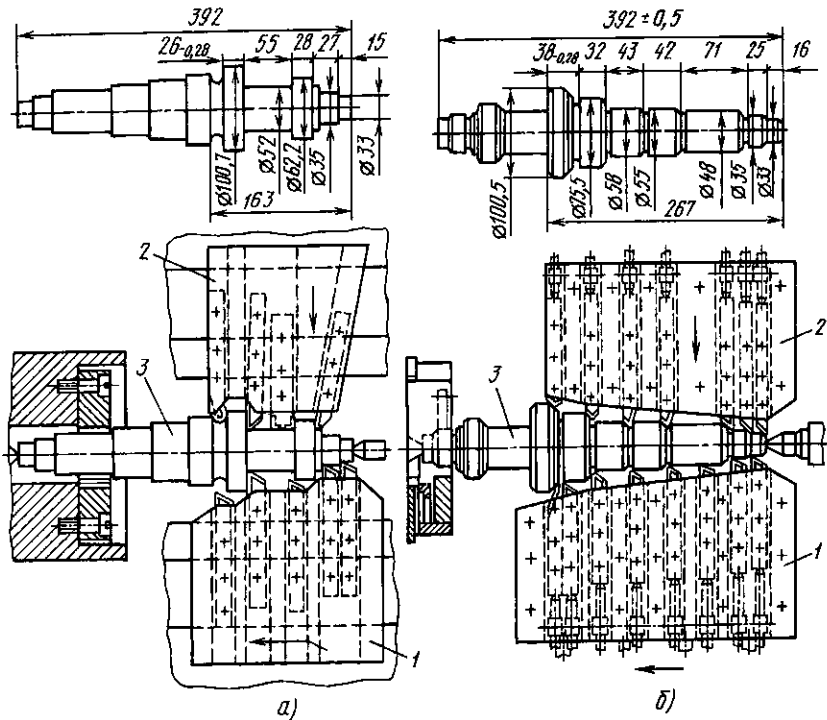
Схема обработки детали на многорезцовом одношпindleльном полуавтомате: *а* – предварительная обработка одного конца заготовки; *б* – окончательная обработка другого конца заготовки; 1 – продольный суппорт с инструментами; 2 – поперечный суппорт с инструментами; 3 – заготовка
